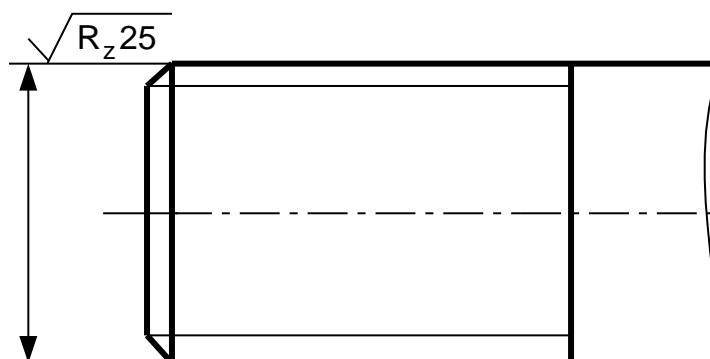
Обозначение шероховатости поверхности профиля резьбы
